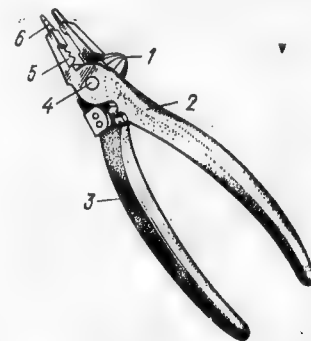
1 — нож для откусывания проводов; 2 — рычаг правый; 3 — рычаг левый; 4 — ось; 5 — прижим с ножами для снятия изоляции; 6 — носок ступенчатый для изготовления колец
